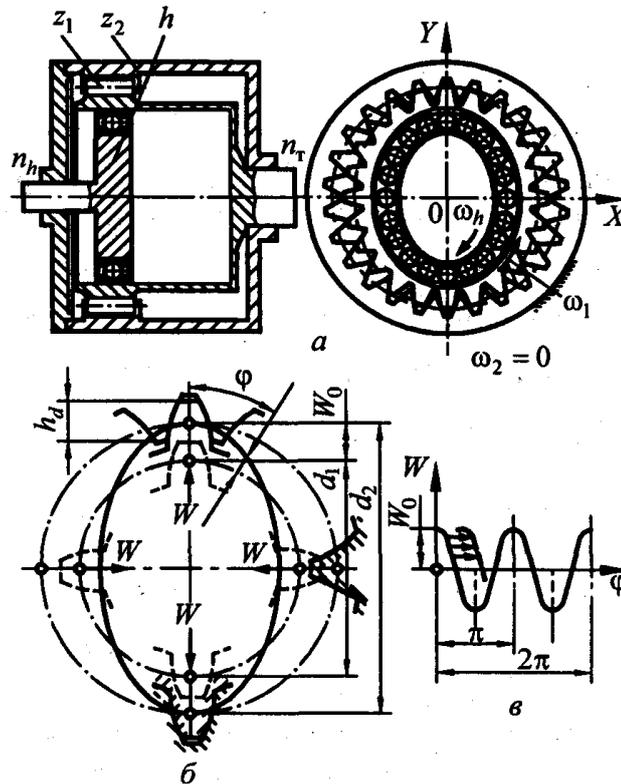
Волновая зубчатая передача: а – конструктивная схема; б – процесс деформации гибкого зубчатого венца; в – перемещения зубьев
